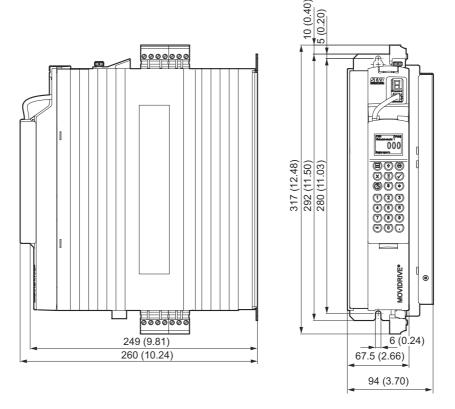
Dimensões MDX60B, tamanho 0M com resistência de frenagem, em mm (in)
